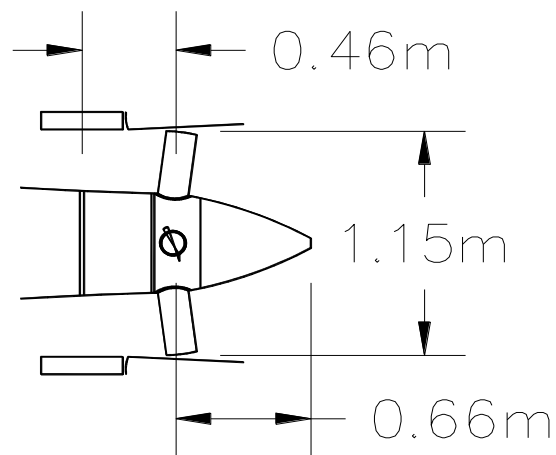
Principales dimensiones del Rodete de la unidad U2, en m.
